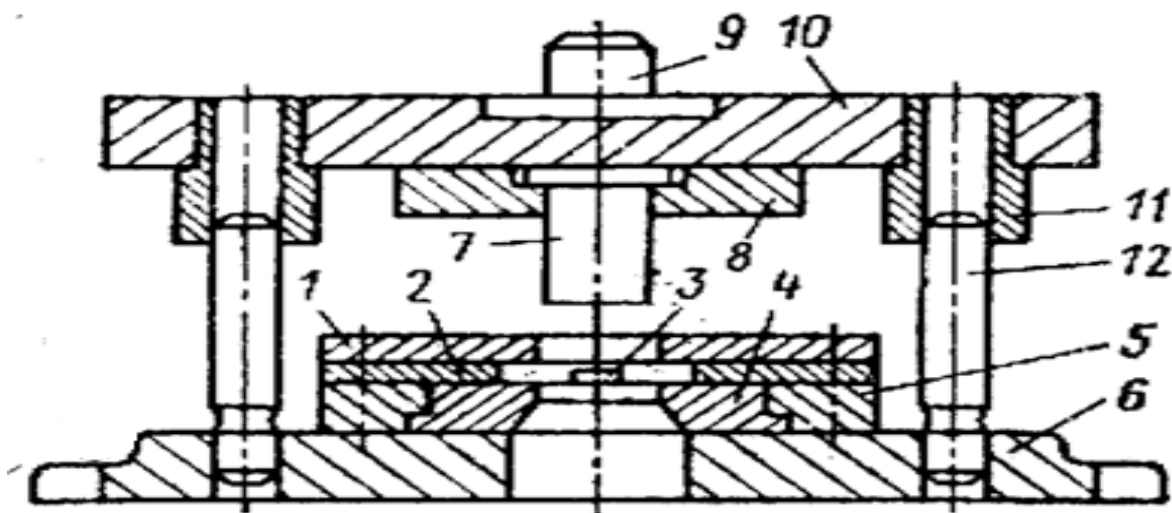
Схема вырубного штампа: 1 - съемник; 2 - направляющие линейки; 3 - упор; 4 - матрица; 5 - матрицедержатель; 6, 10 - нижняя и верхняя плиты; 7 - пуансон; 8 - пуансонодержатель; 9 - хвостовик; 11 - направляющие втулки; 12 - направляющие колонки
